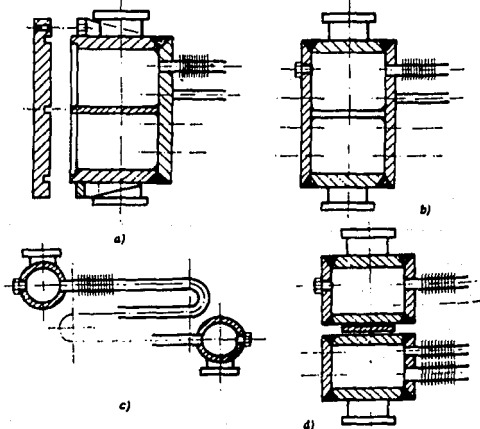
Tipos de cabezales. a) Con tapa desmontable. b) Soldado con tapones. c) Cilíndrico. d) Partido.
